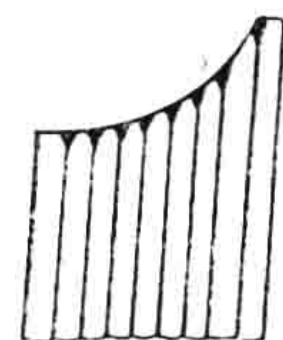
环焊缝坡口堆焊止裂焊缝
